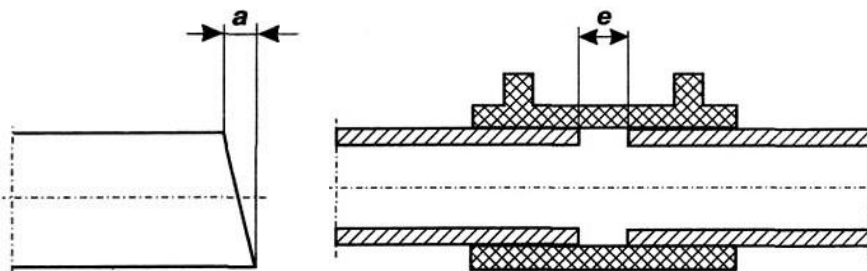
Схема сборки: a – максимальный допуск косо́го среза трубы; e – максимальный зазор между двумя концами труб в муфте
